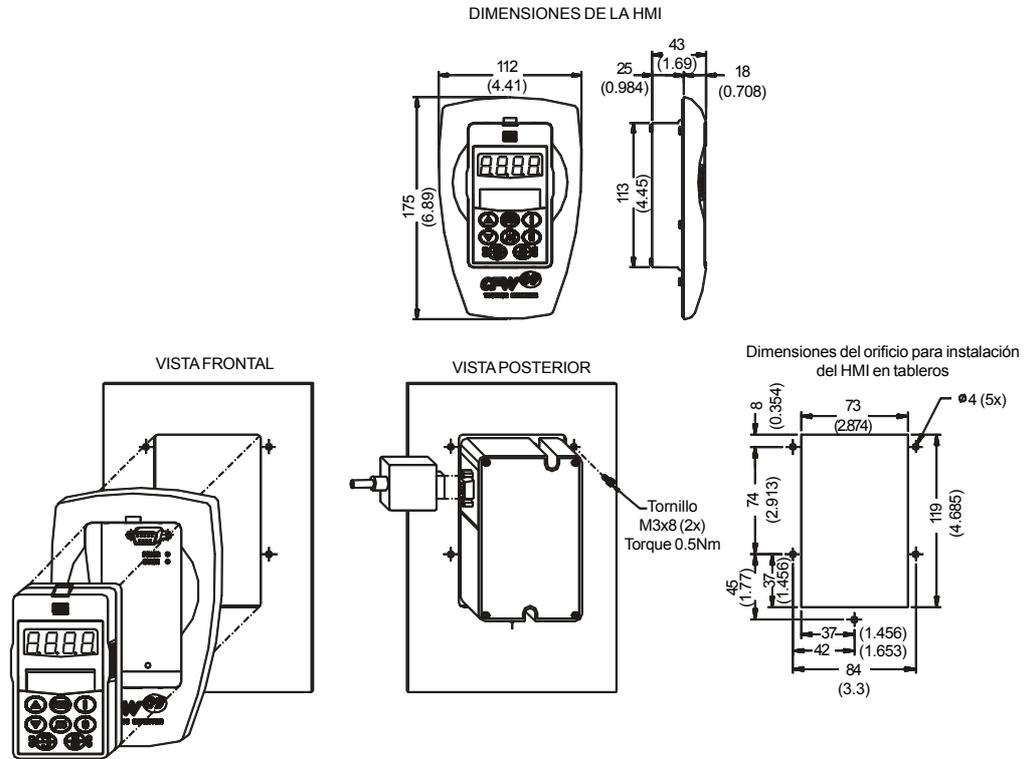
a) - Dimensiones en mm (in) y como instalar en el tablero HMI y Moldura
